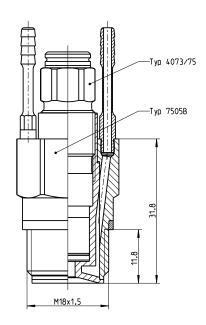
Einbau des Sensor Typs 4075A... in Kühladapter Typ 7505B
